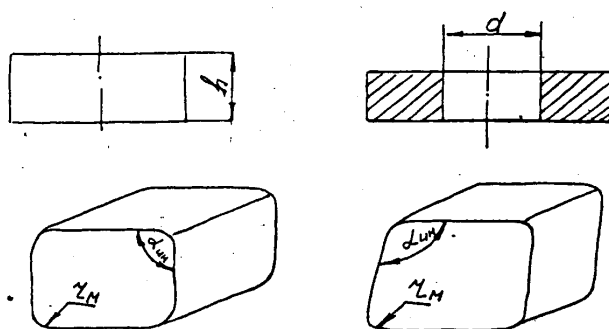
Формоблоки для операций вырубке, пробивки, гибки
